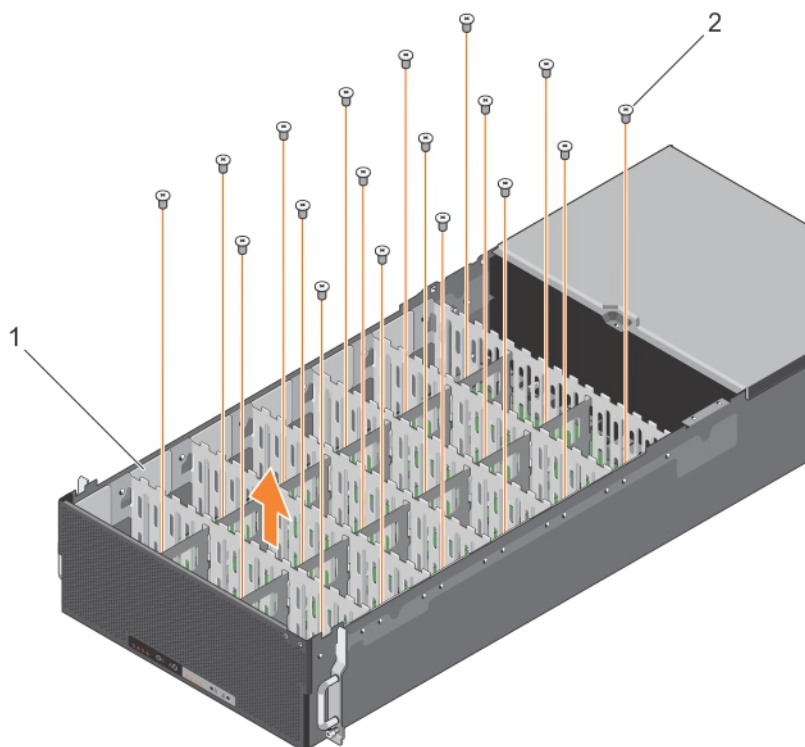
Entfernen und Installieren des Festplattengehäuses
